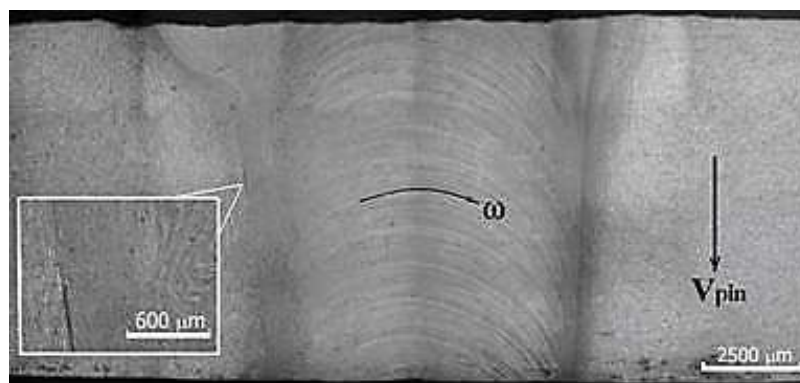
Нижняя часть сварного шва. Слой толщиной 0,6 мм снят путём фрезерования
